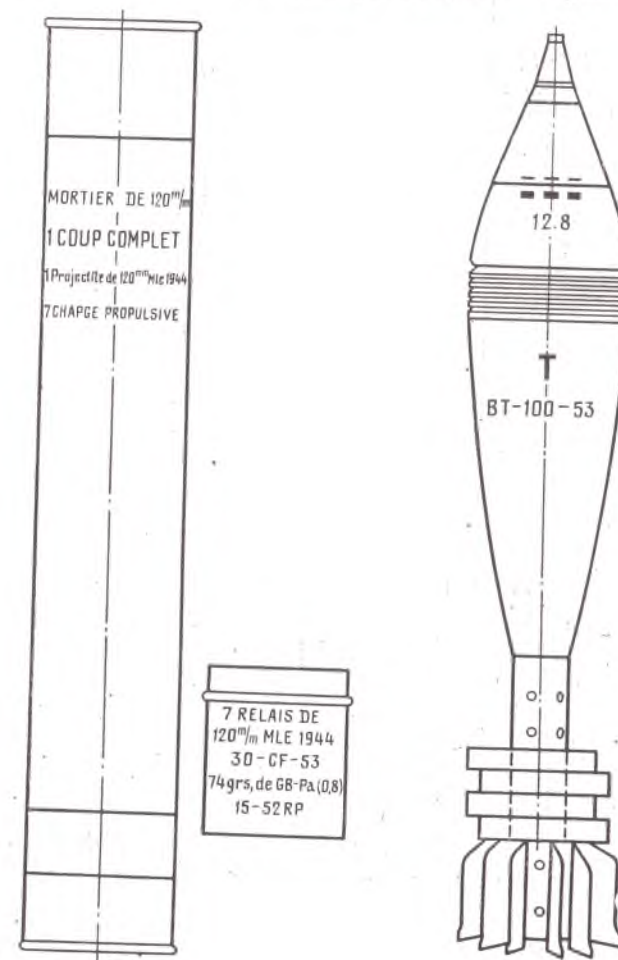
Образец маркировки мины М44, пенала для выстрела и упаковки для зарядов
